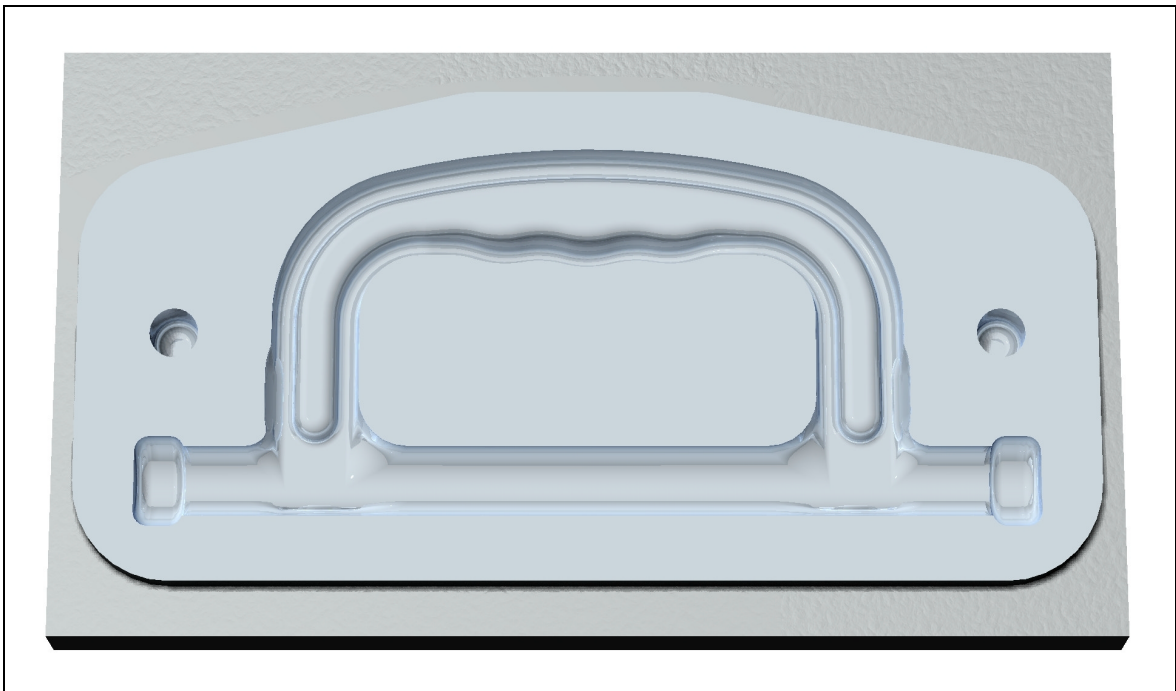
Formwerkzeug der Griffe des CCB3
